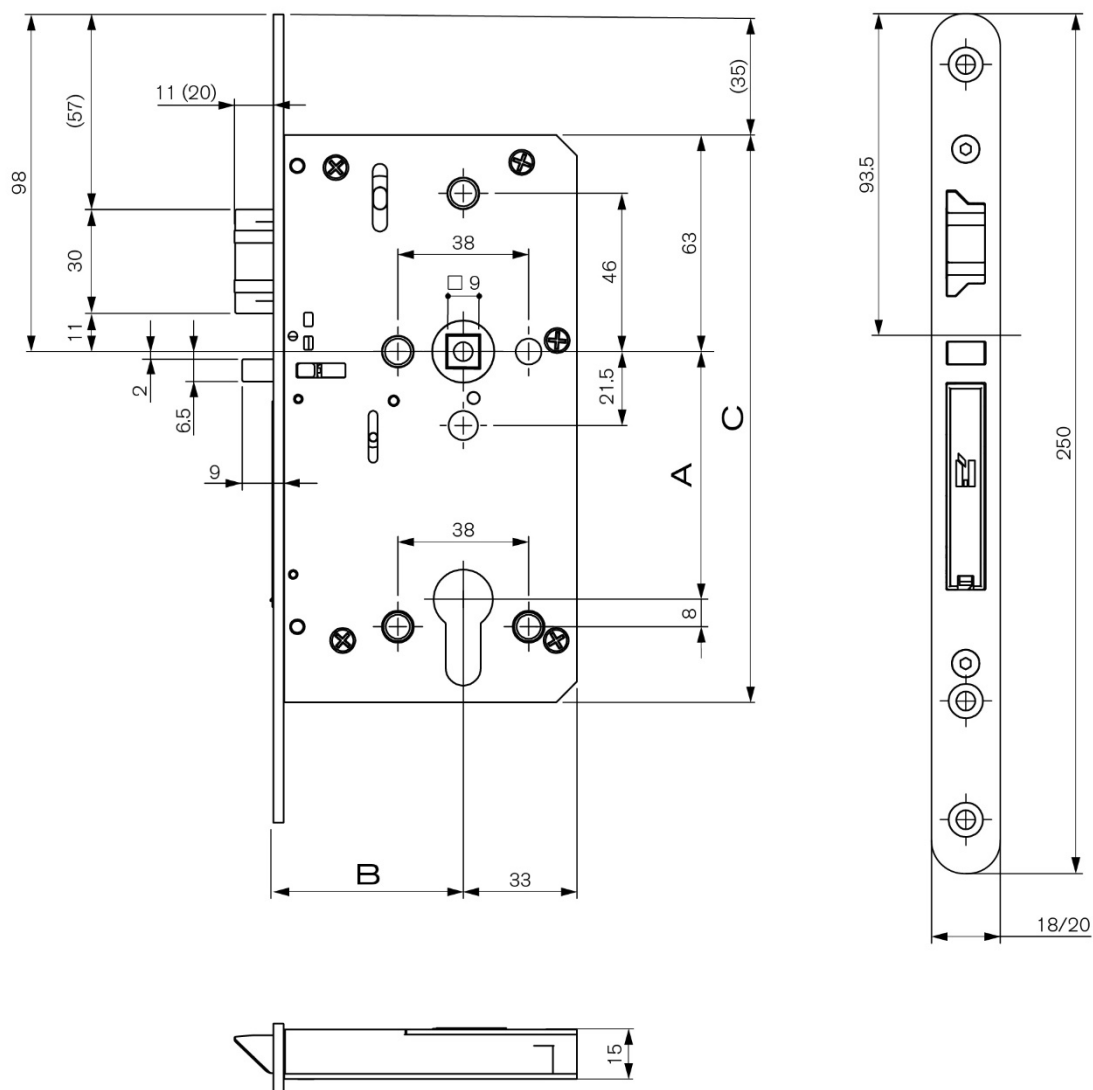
Abmessungen für Schlossinstallation – Profilzylinder 88
